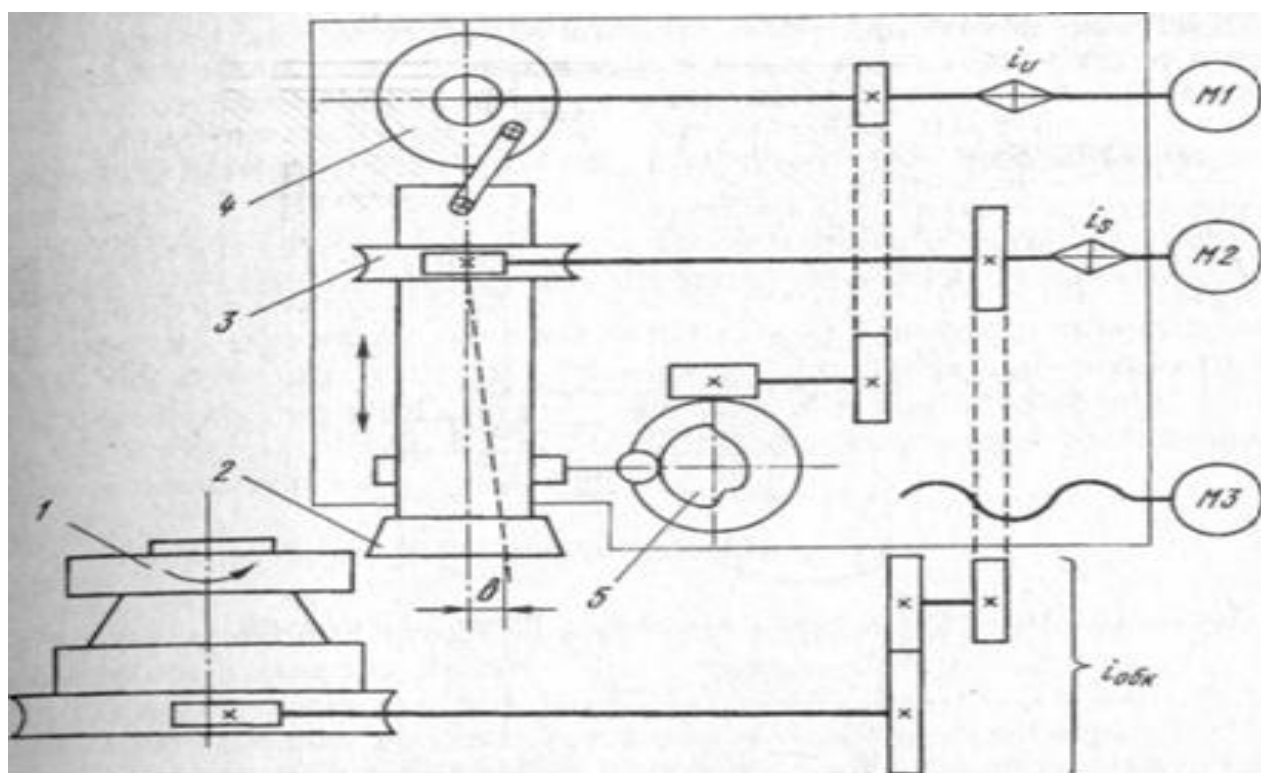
Кинематическая структура зубодолбежного станка.
